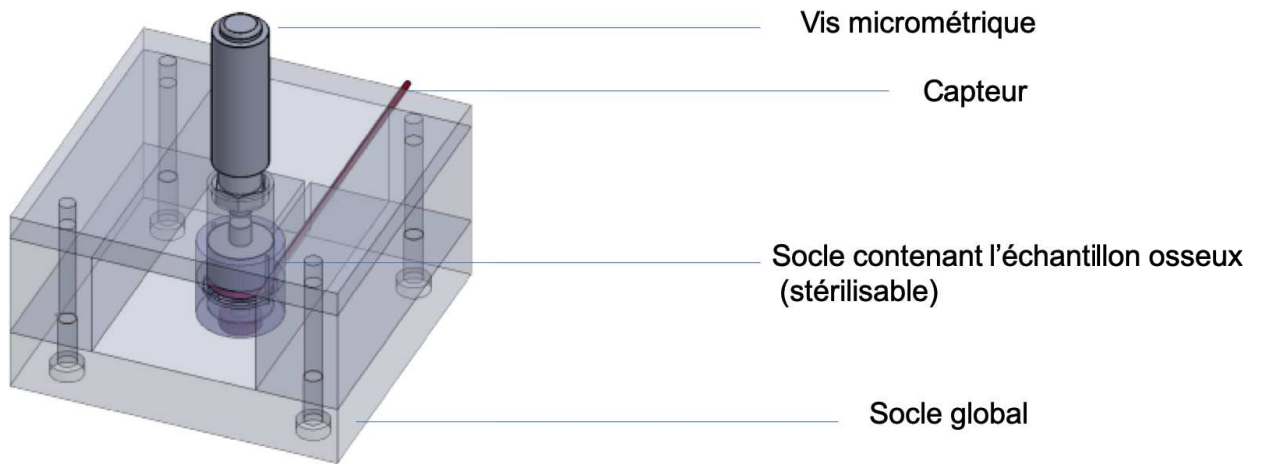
Schéma définitif avant usinage (il manque le joint sur ce schéma) – Vue globale
